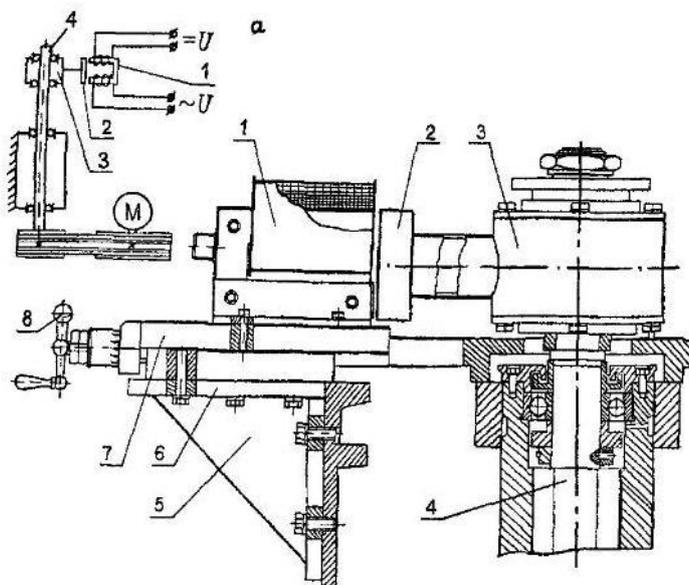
Электромагнитное нагрузочное устройство для испытаний фрезерных шпинделей
